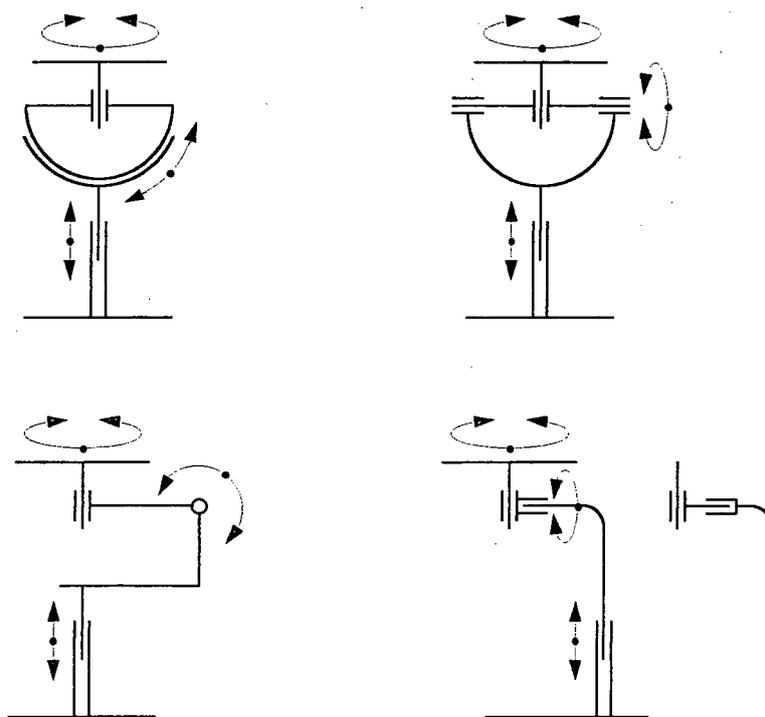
8 Princípios de solução para posicionador para soldas. [15]
